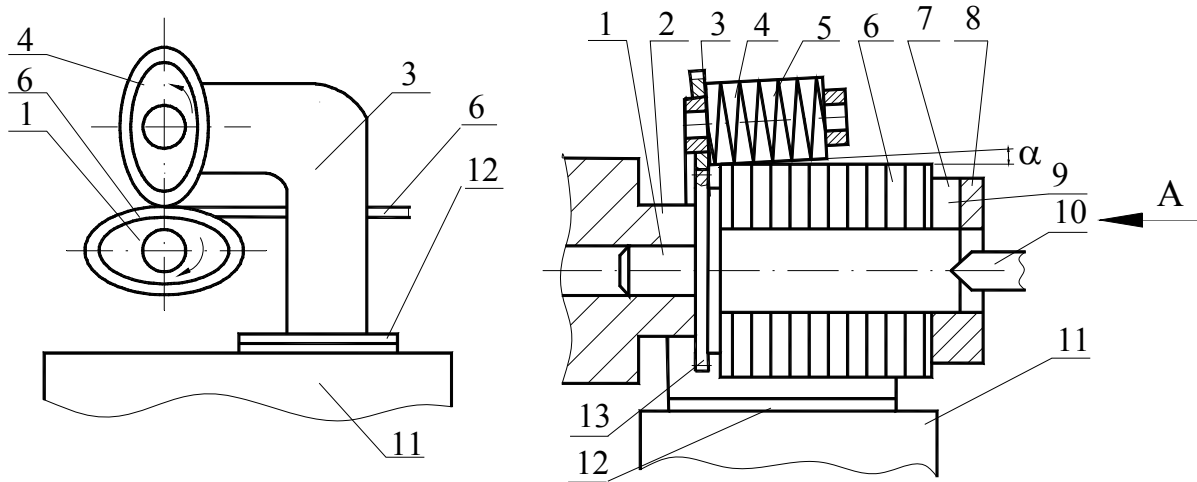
Схема пристрою для виготовлення збірно зубчасте навивне колесо
